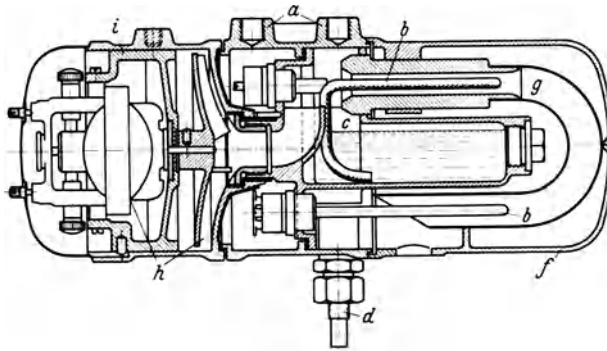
Schnittbild des Gebers zum Feuchtigkeitsmesser (S & H) (69). a Augen für Befestigung; b Thermometer, befeuchtet und trocken; c Wasservorratsbehälter; d Wasserzufluß; f Gehäusekappe; g Luftführungsrohr; h Lüftermotor mit Lüfterrad; i Lüftergehäuse.
